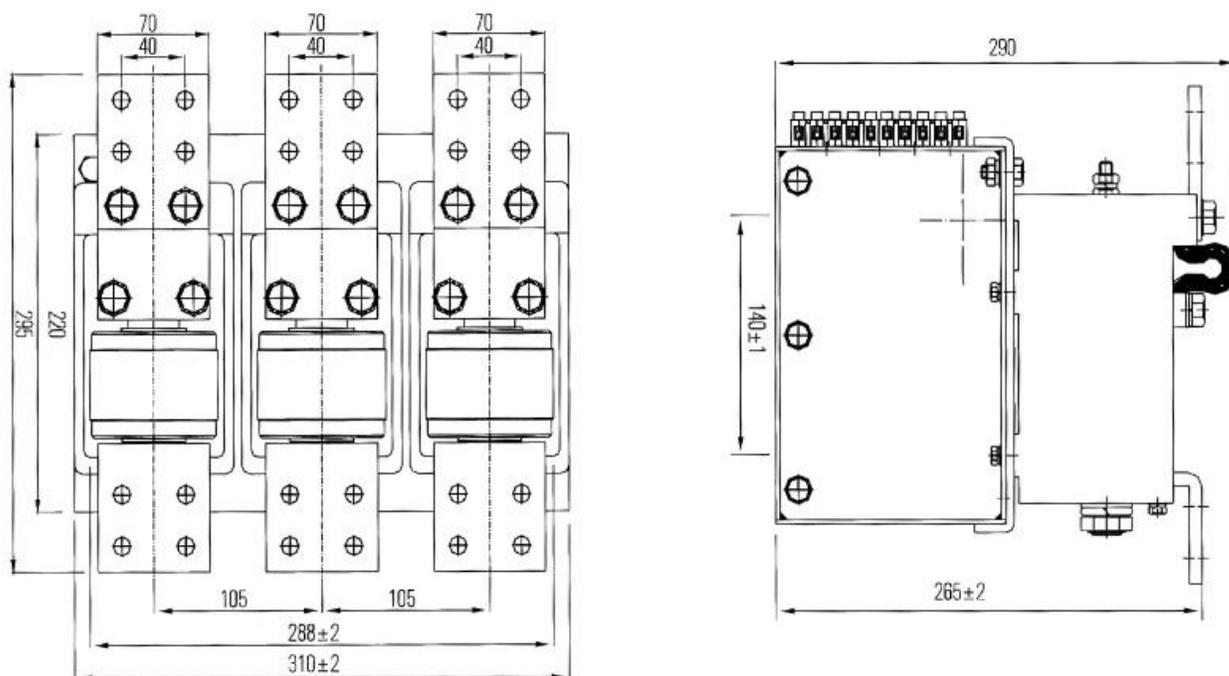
Габаритные размеры КВТ-1,14-1000/1250
